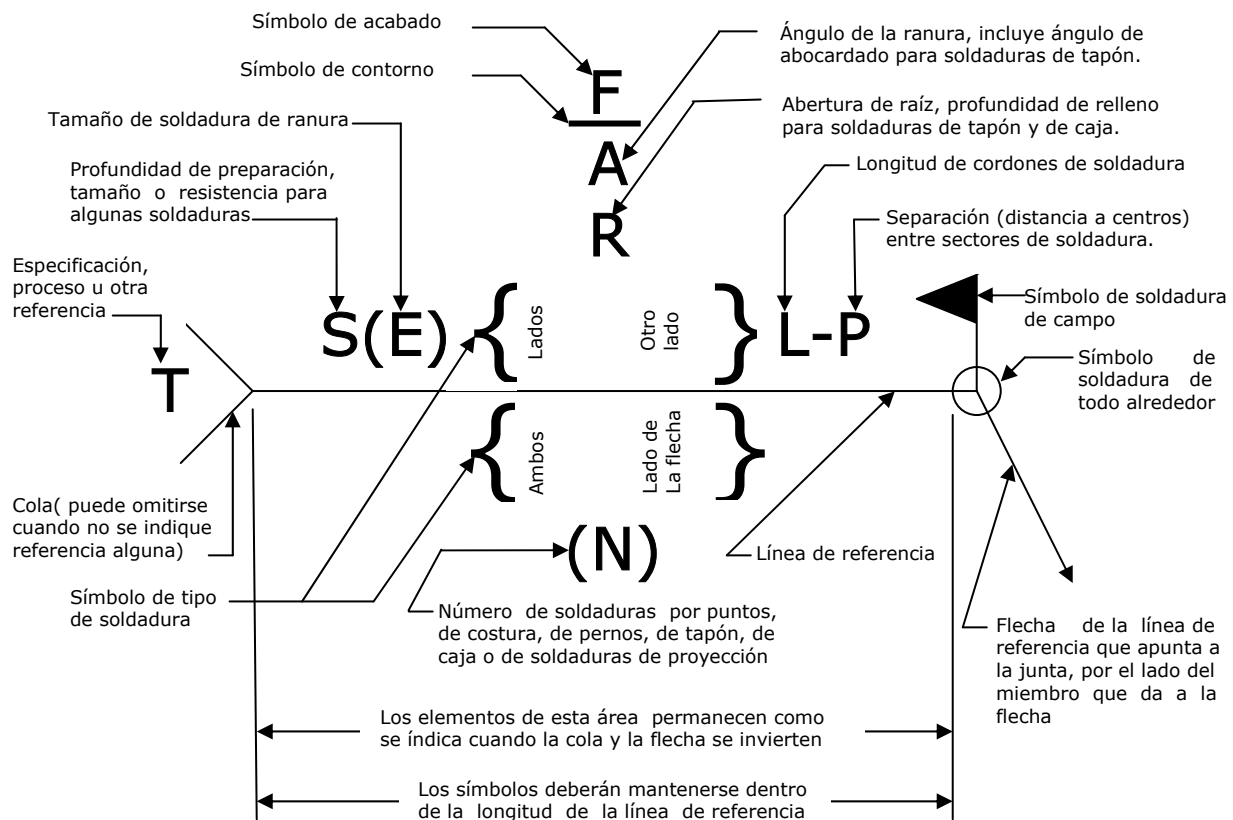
Localización de cada elemento en un símbolo de soldadura, de acuerdo a la ANSI/AWS A2.4
